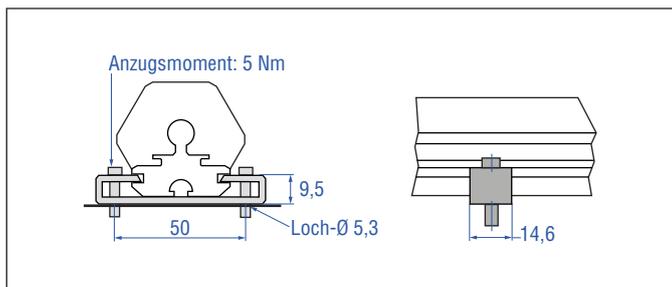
Montageklammern (Artikelnr. 400 802) mit Zylinderschraube M5×20
